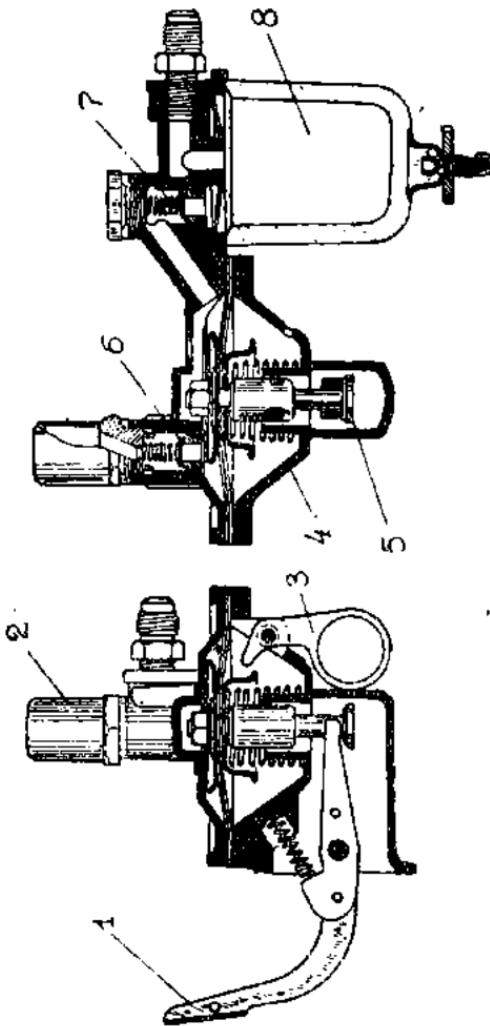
Бензиновый насос. (1 — рычаг привода; 2 — демпфирующий колпачок; 3 — рычаг ручной подачки топлива; 4 — корпус; 5 — шток и диафрагма в сборе; 6 — выпуск; 7 — выпускной клапан; 8 — выпускной клапан).
